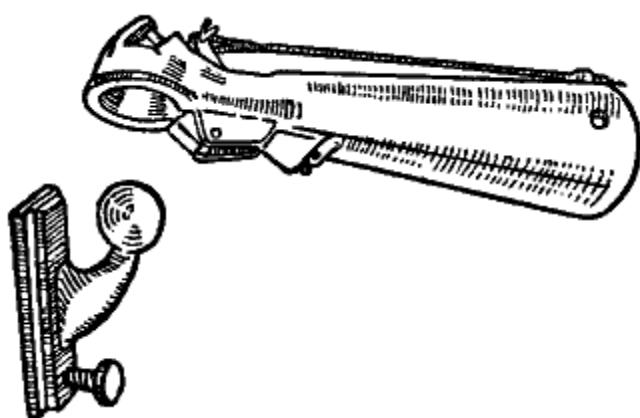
Современная оковка нока спинакер-гика и оковка для крепления его к мачте
